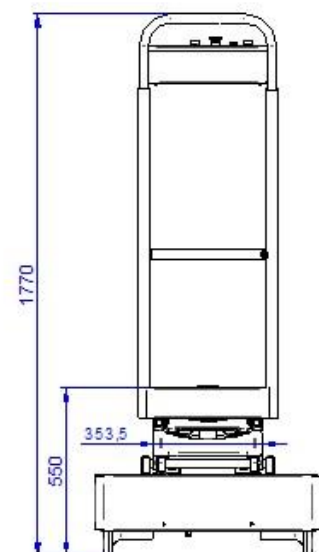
; Dimensions de la hauteur minimale en mm, 2 pantographes
